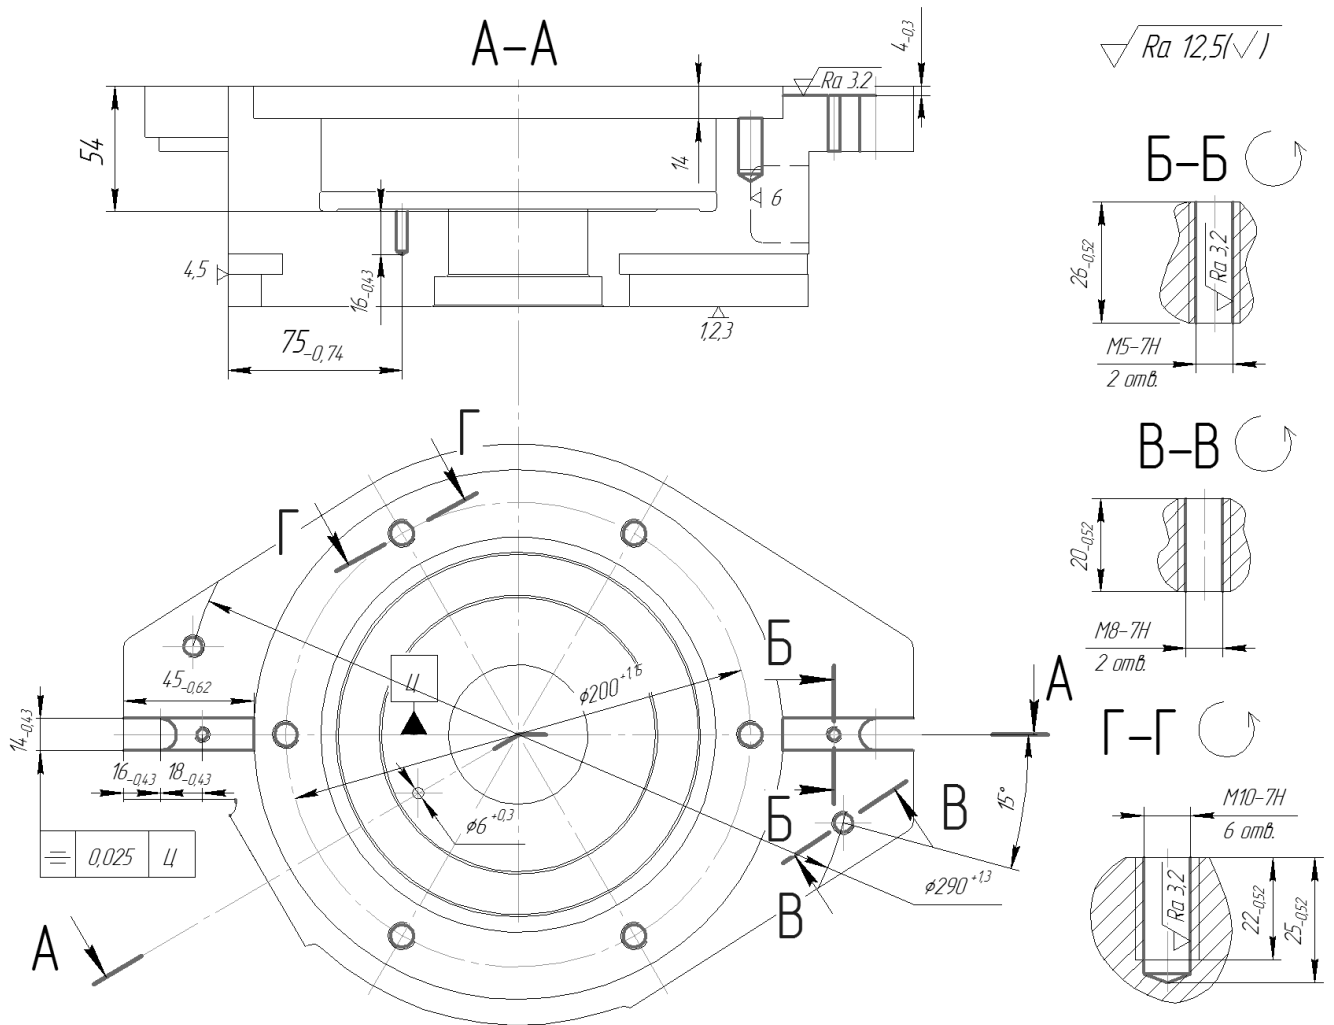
Ескіз обробки заготовки на операції 050
